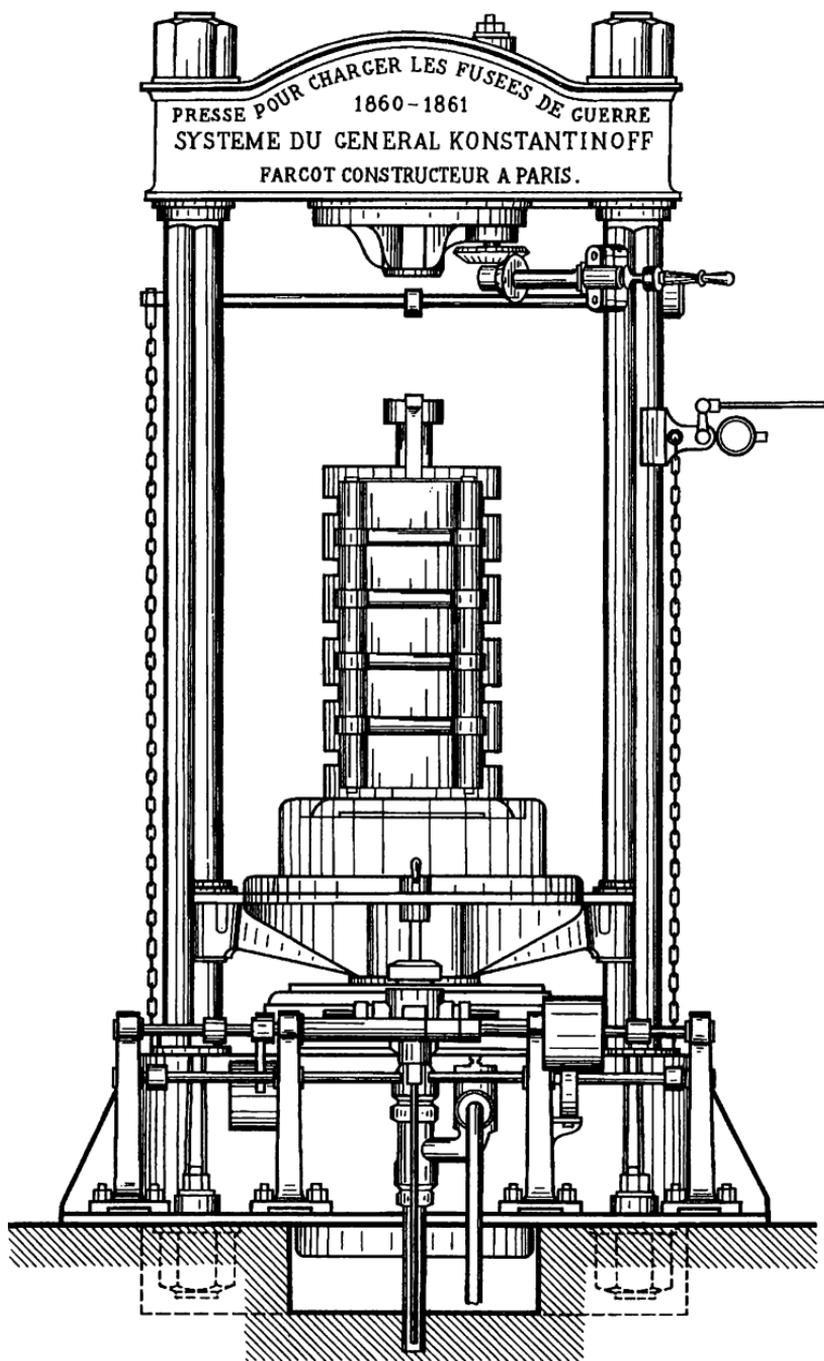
Гидравлический пресс конструкции К.И. Константинова
